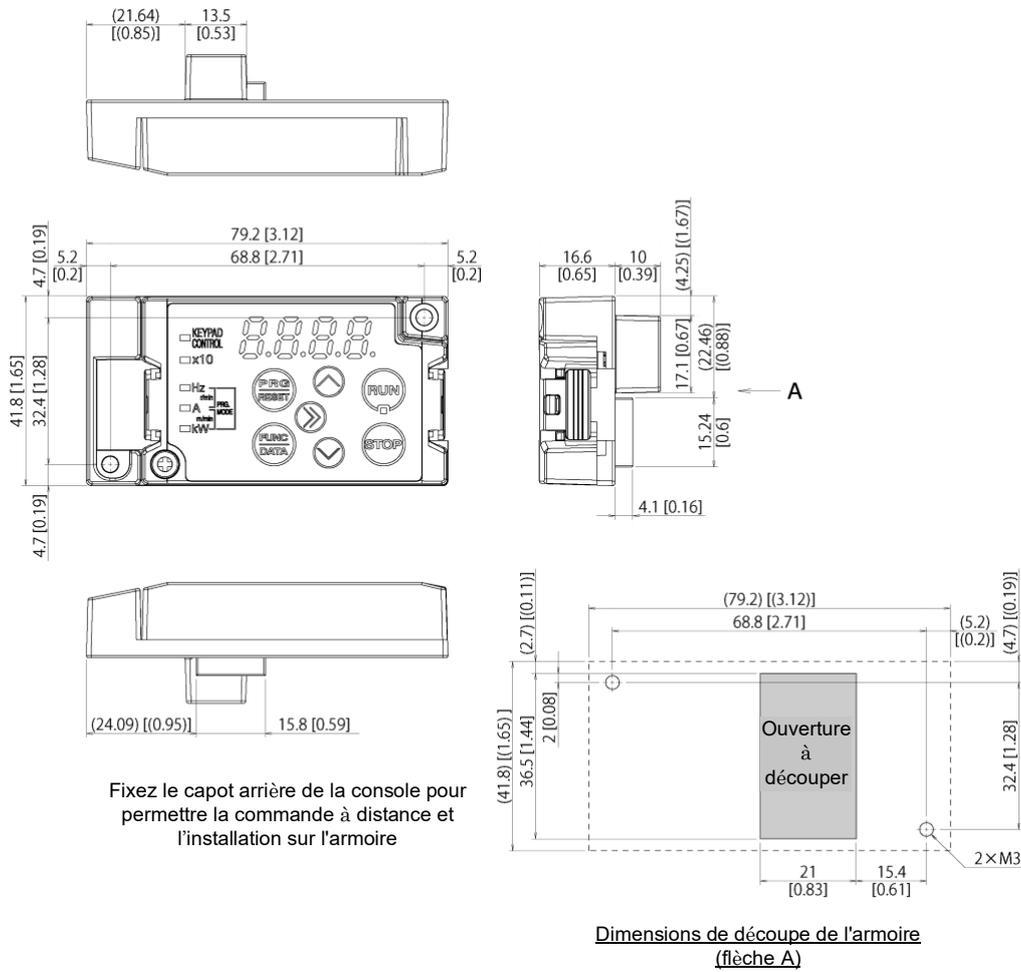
Emplacement des vis de fixation et dimensions de découpe de l'armoire
